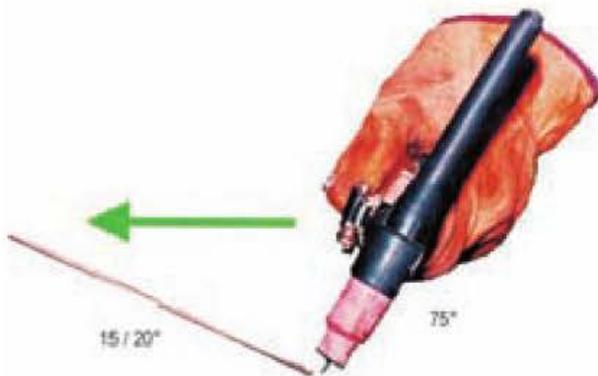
Dirección y posición de la soldadura TIG.
